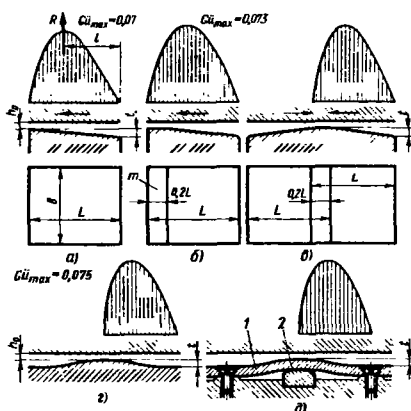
Схемы подшипников с наклонными опорными поверхностями
